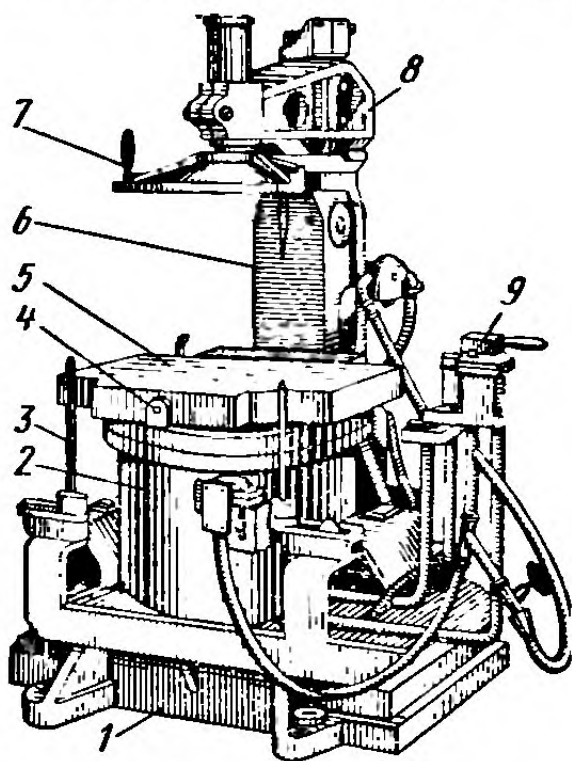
Вибропрессовая формовочная машина модели 226
